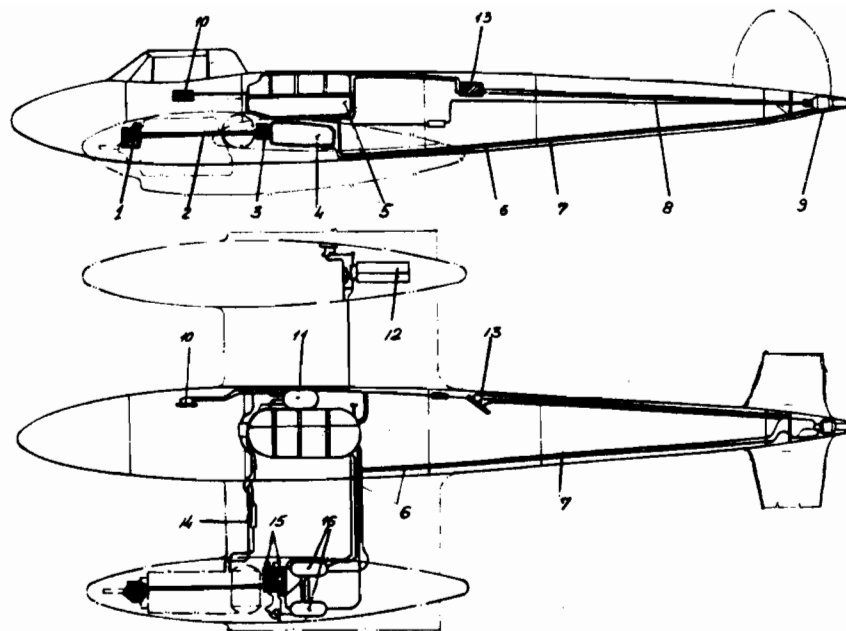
Компоновка реактивной установки РY-1 с двигателем РД-1 на самолете Пе-2:
